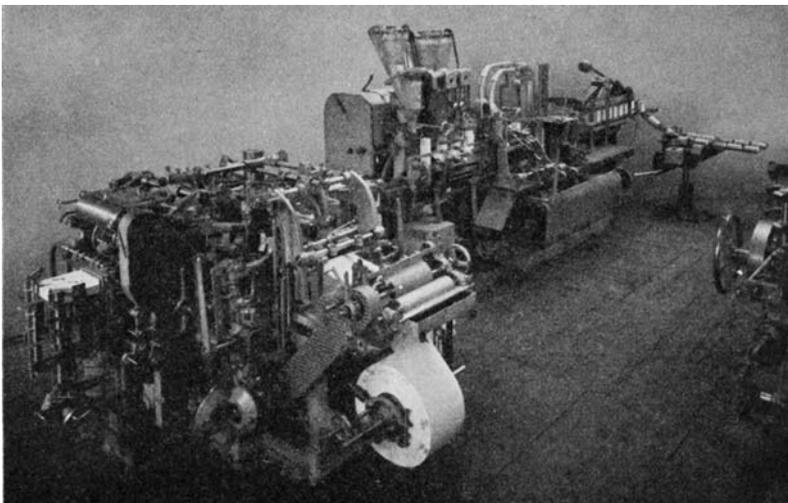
Füll- und Packmaschinengruppe (Fr. Hesser, Maschinenfabrik A G., Stuttgart-Cannstatt).
